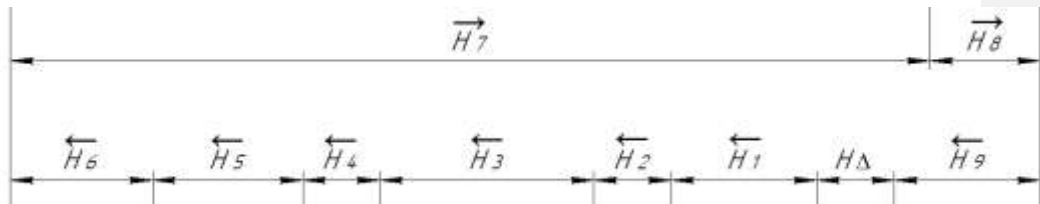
Схема складального розмірного ланцюга вала зубчастого колеса
